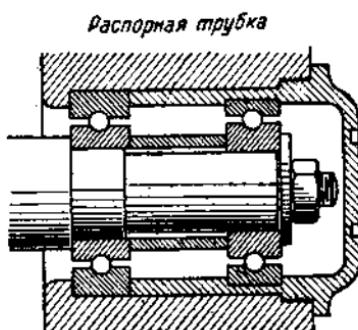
Посадка обоймы шарикоподшипника помо- щью распорных втулок.
